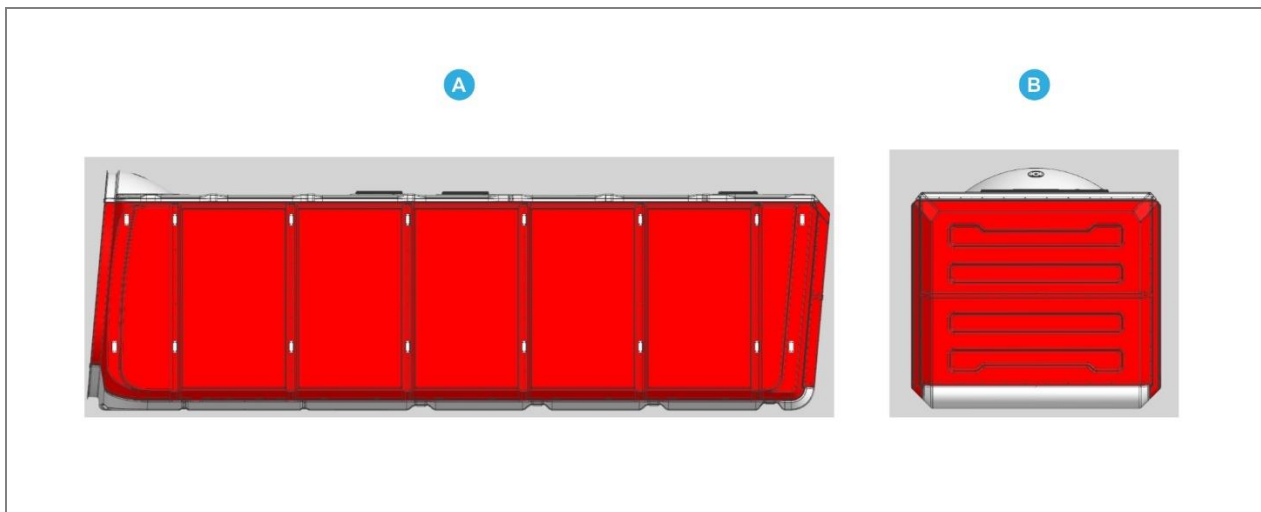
Beispiel eines Delta4000-Maschinenhauses mit roter Tageskennzeichnung
